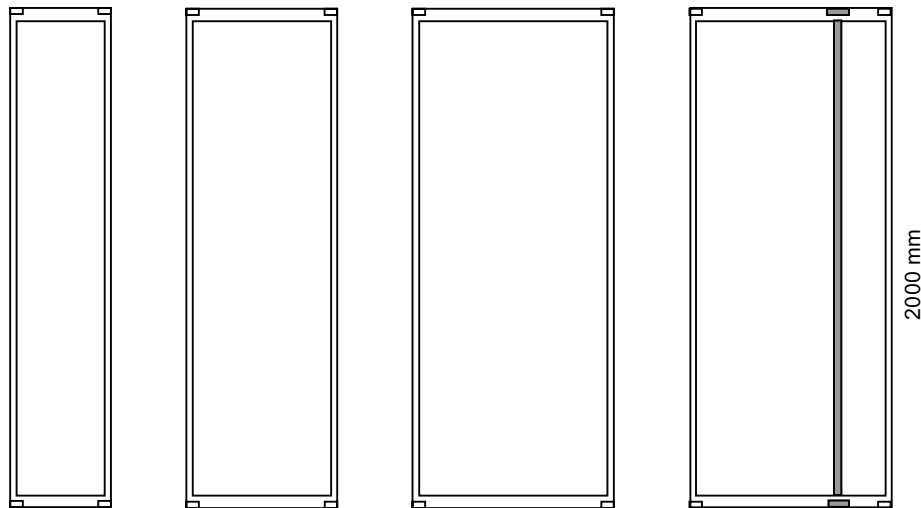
Frontansicht von Gerüsten mit Trägersbau
